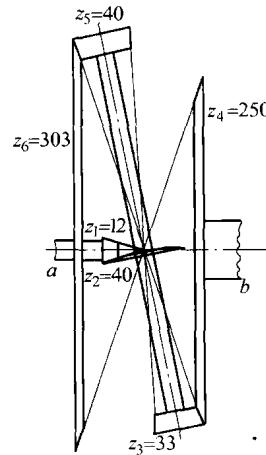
传动比 $i = 262500$ 的行星齿轮传动装置
